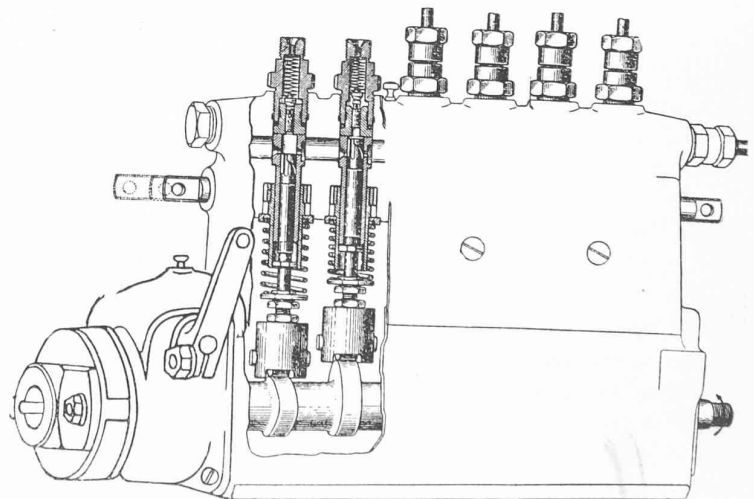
Vue et coupe partielle de la pompe à combustible Bosch.
